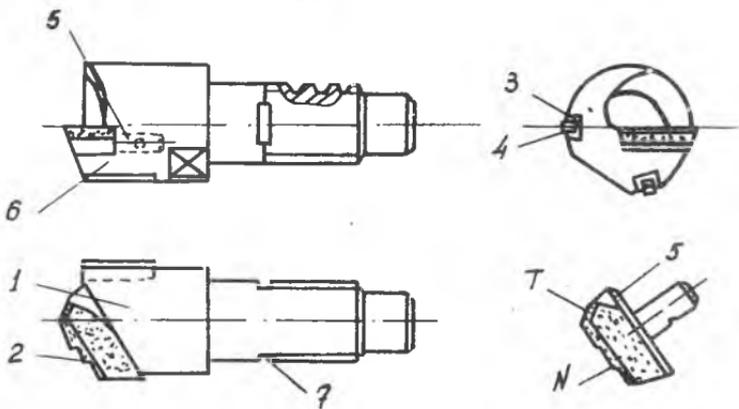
Сверлильная головка 1 - корпус, 2 - твердосплавная режущая пластина; 3 - колодка крепления направляющей; 4 - направляющая пластина; 5 - сменный резец, 6 - опора резца
